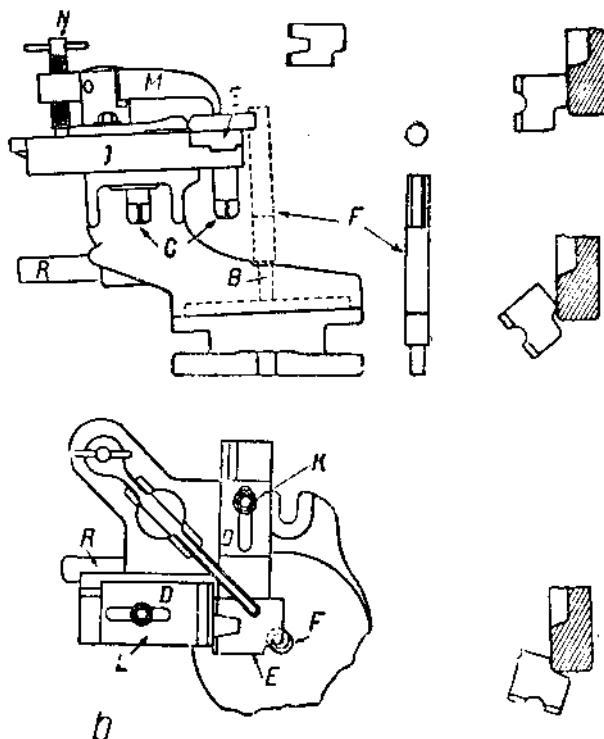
Детали приспособления для заточки резцов Дэвис.
